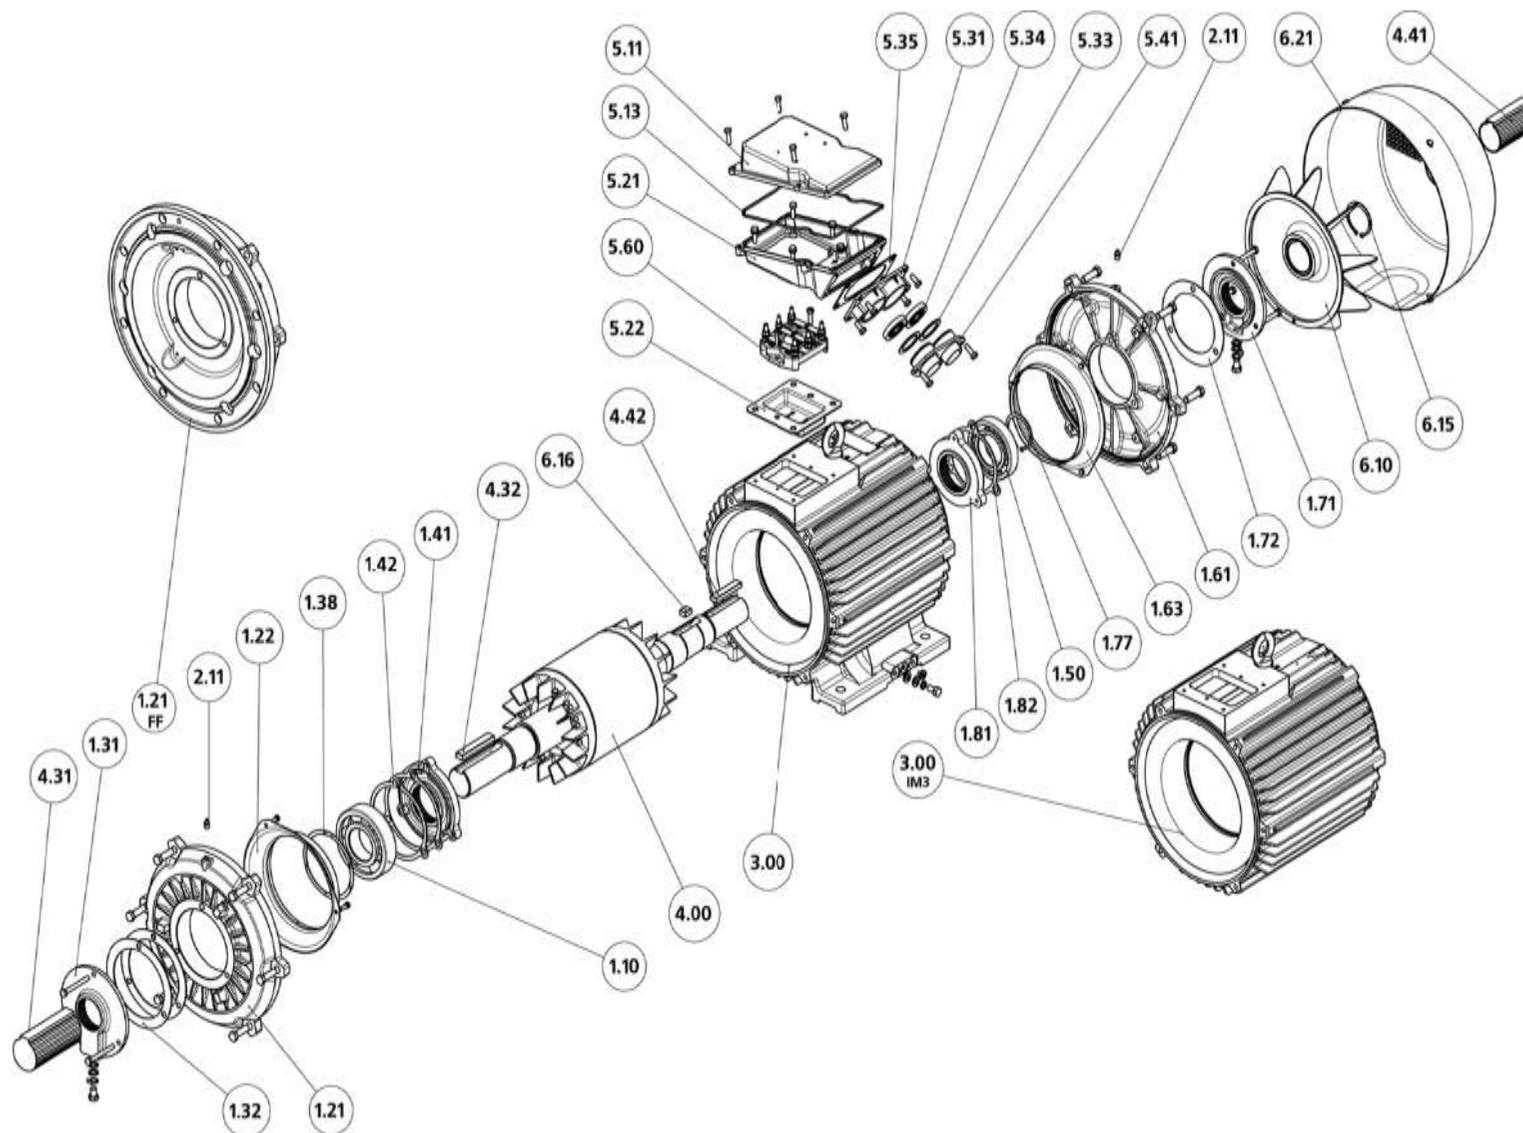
Конструкция, основные узлы и детали двигателей с высотой оси вращения 160–280 мм, степень защиты IP5
